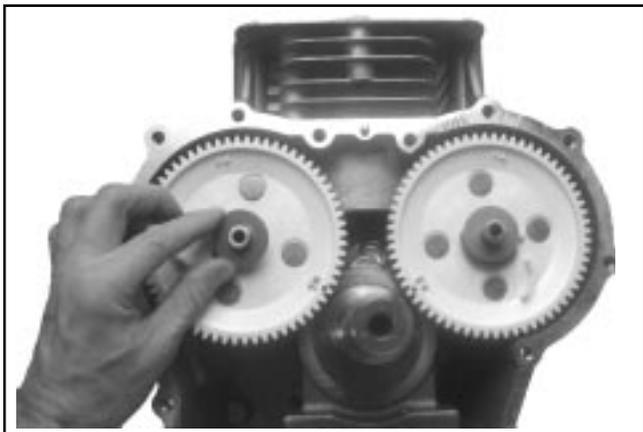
Installation de l'engrenage à cames côté admission et de la rondelle de butée.
